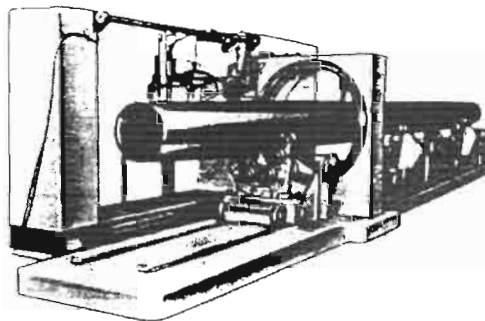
Станок СФРТ-1220 для фасонной резки труб
